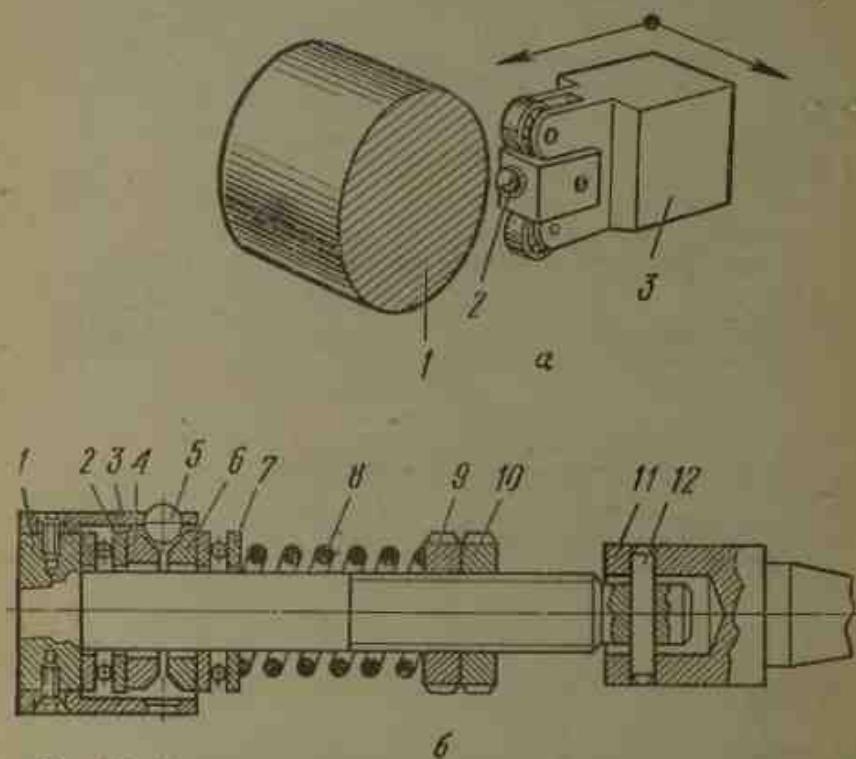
Державка для обкатывания поверхности шариком (а); шариковая раскатка для отверстий (б):
